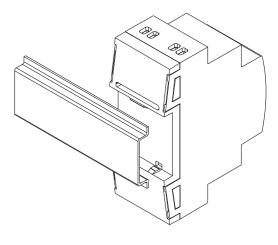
Montaje de FANinBOX 230V 1CH en carril DIN
